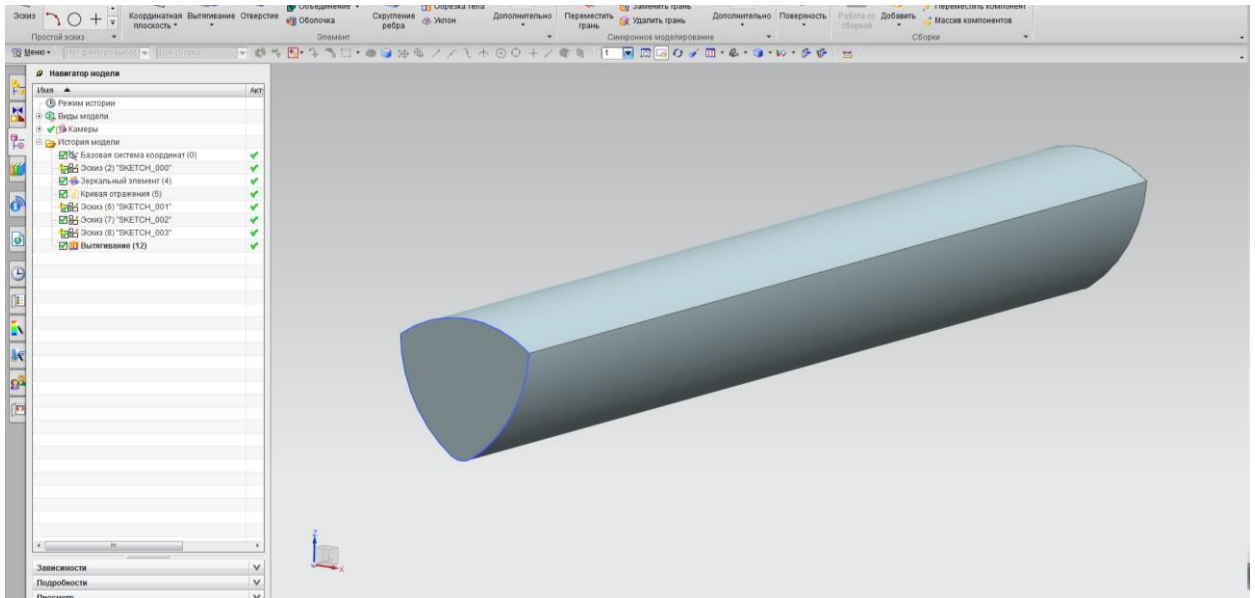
Трехмерная модель сварного шва.
